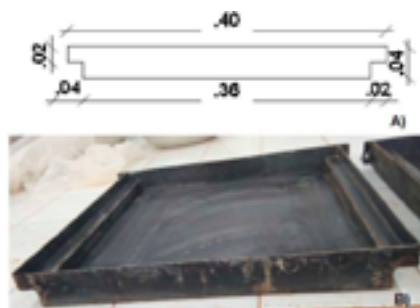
Protótipo 1: A) desenho; B) confeccionado 40cmx40cm
